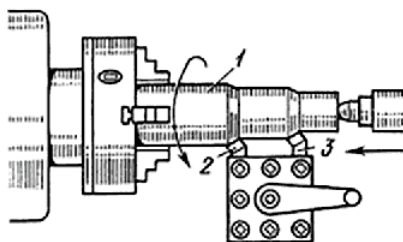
Установка длинных заготовок в патроне с применением заднего центра:
